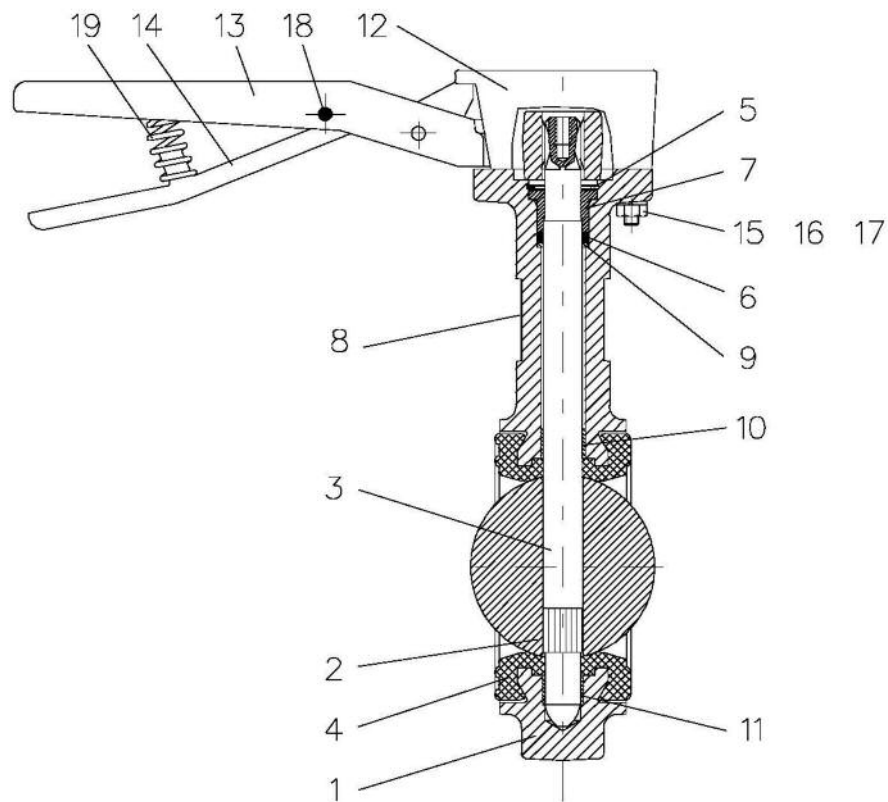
Устройство затвора дискового поворотного типа VFY.
